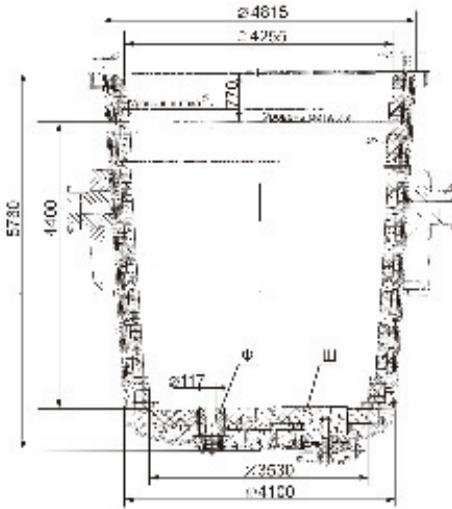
Схема вертикального осевого сечения сталеразливочного ковша КС-350. Ф – щелевая фурма; Ш – шибер.
